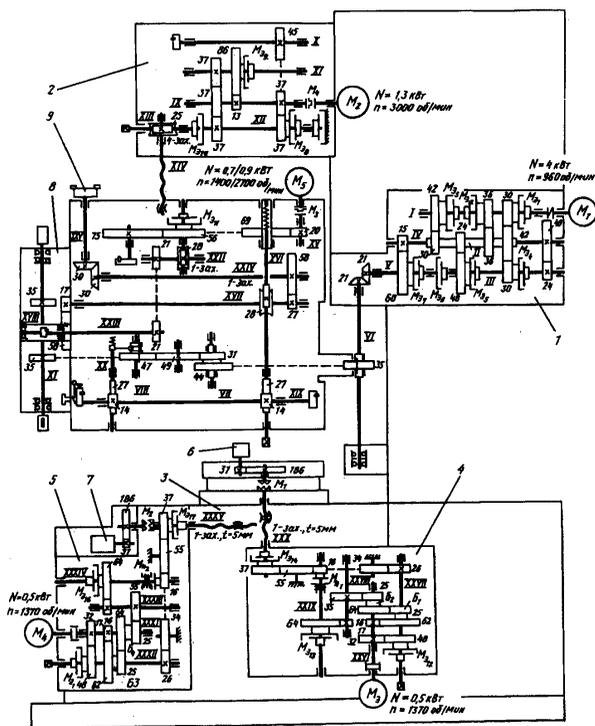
Кинематическая схема вертикально-сверлильного станка с ЧПУ
